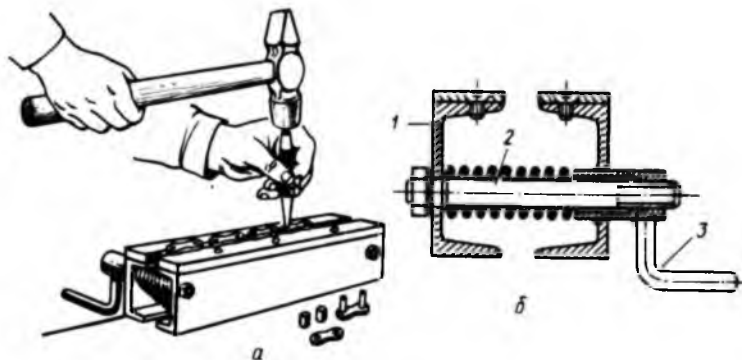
Приспособление для разборки приводных втулочно-роликовых цепей:
